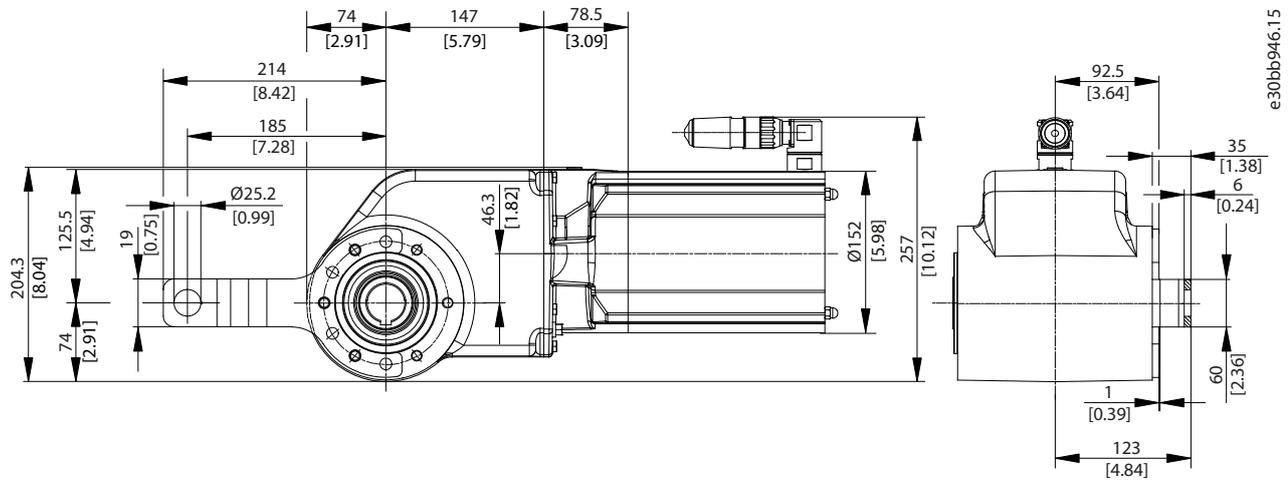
VLT® OneGearDrive® Hygienic com braço de torque na posição frontal (opcional)
